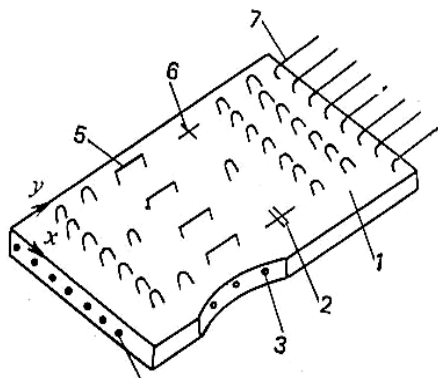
Структура тканого устройства коммутации: 1 – многослойное изоляционное поле, 2, 3 – электропроводящие нити, 4 – монтажные узлы,
